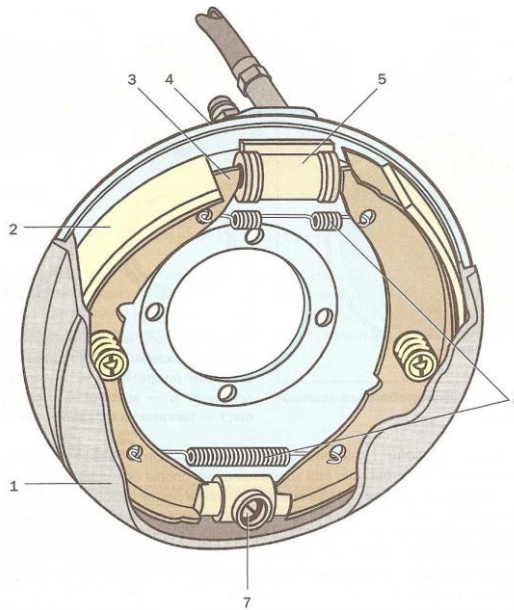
Барабанний механізм з рівними приводними силами і одностороннім розташуванням опор колодок:
